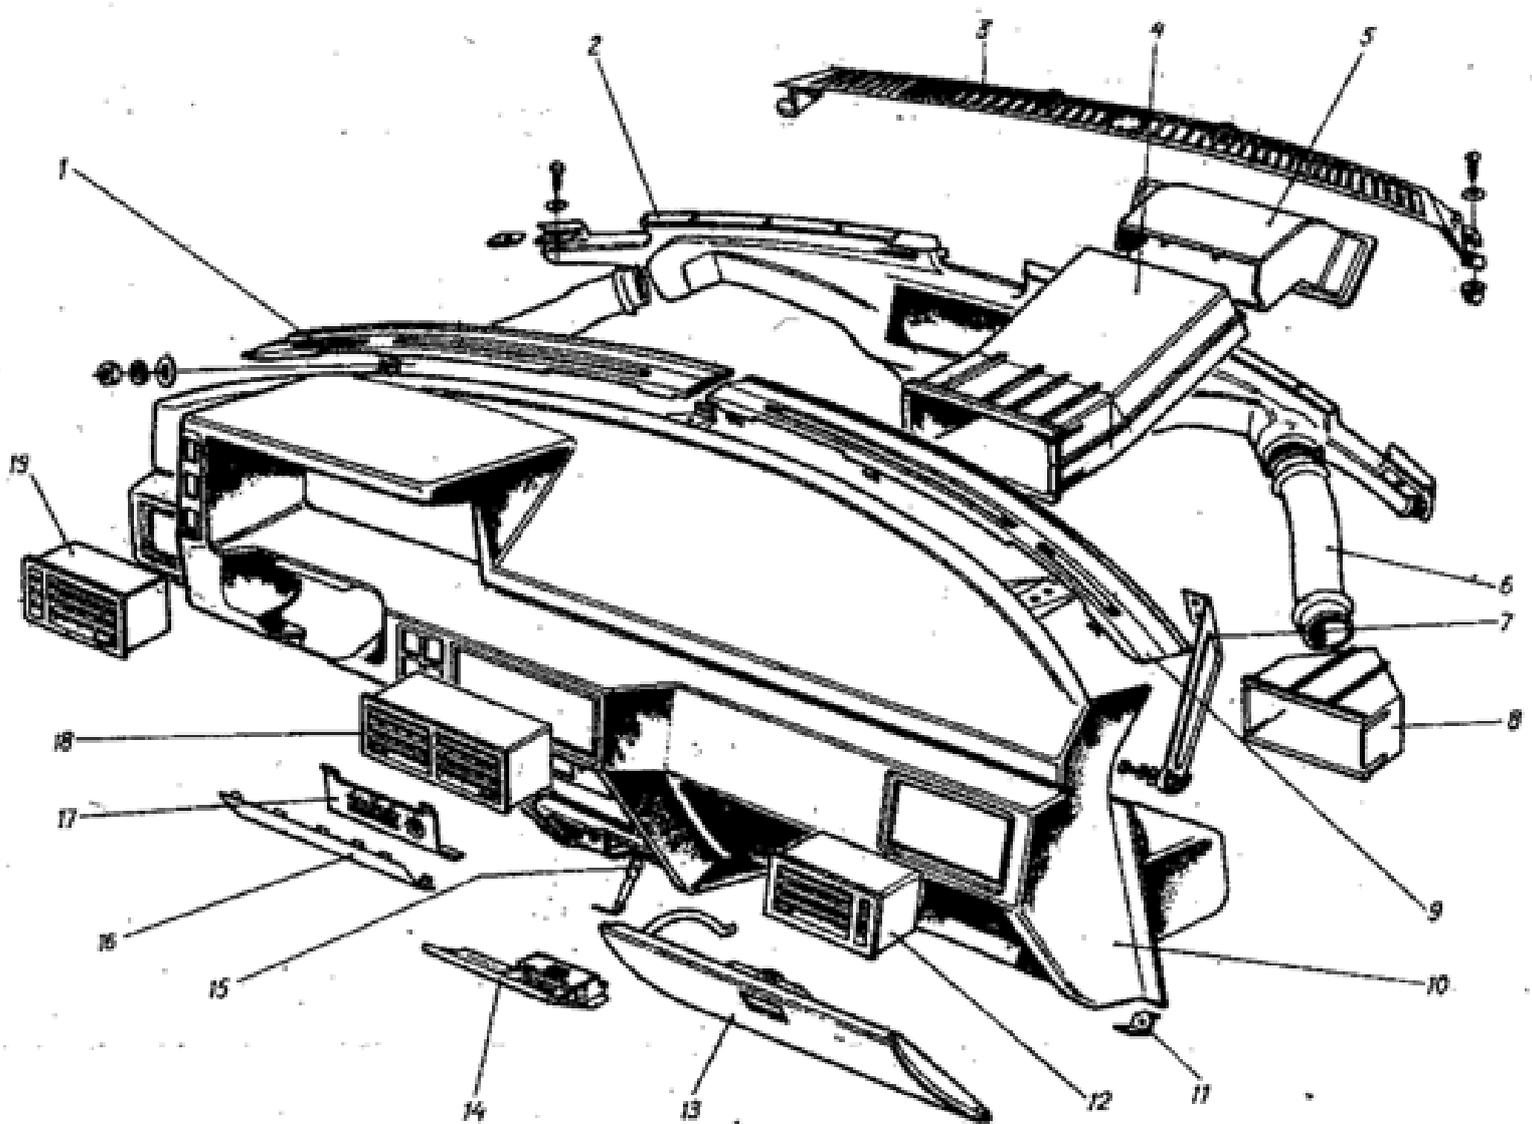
Детали панели приборов 11021-5325016: 1 - накладка левая; 2 - сопло обдува; 3 - облицовка панели; 4 - корпус центральный; 5 - наставка; 6 - патрубок; 7 - кронштейн боковой; 8 - корпус боковой правой; 9 - накладка правая; 10 - панель приборов; 11 - кронштейн боковой; 12 - рамка боковая; 13 - дверца ящика; 14 - крышка пепельницы; 15 - кронштейн центральный; 16 - крышка блока предохранителей; 17 - вставка; 18 - рамка центральная; 19 - рамка боковая.
